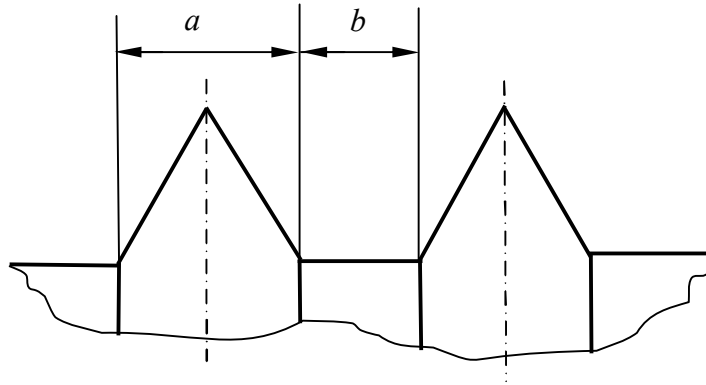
Схема барабана: a – ширина конусного колеса; b – ширина циліндричної вставки
